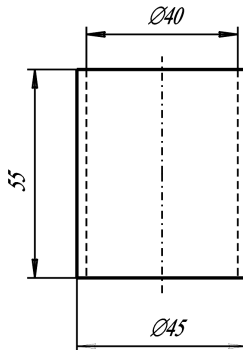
Заготовка для виготовлення безступеневого пуансона
